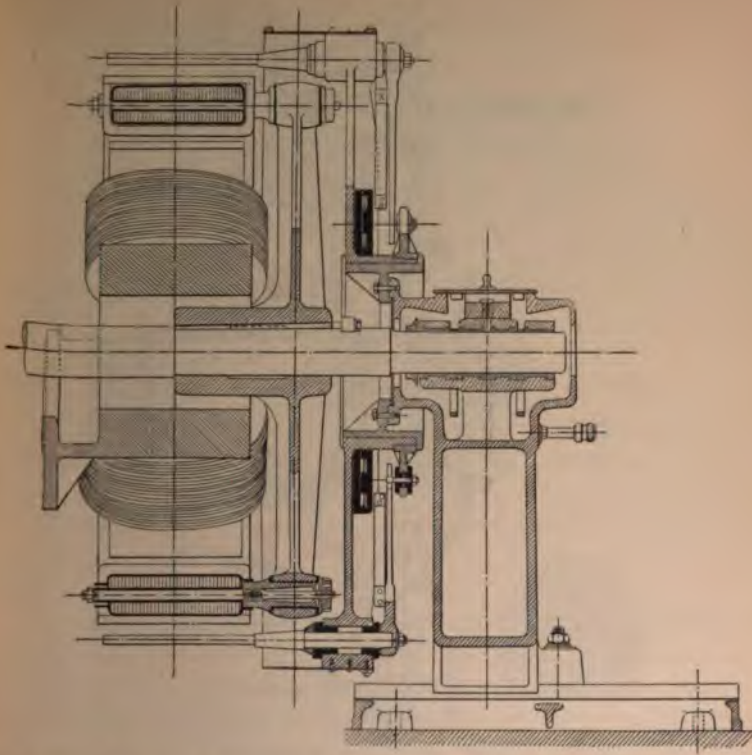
Société Alsacienne (Siemens & Halske): Innenpolmaschine.
